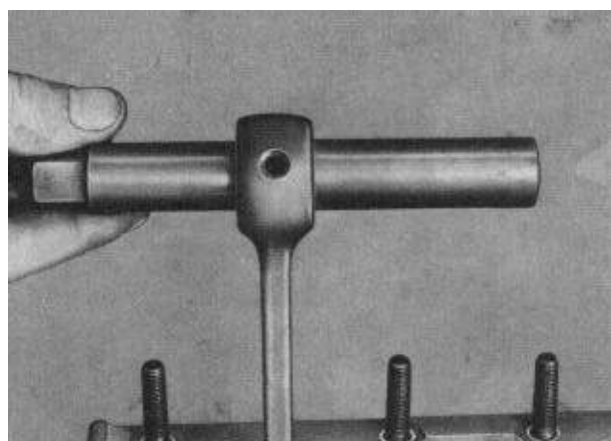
Bohrung mit Kontrolldorn überprüfen
